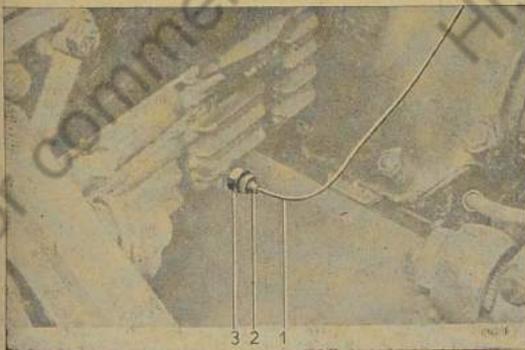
Fühler für Öl-Fernthermometer abschrauben
